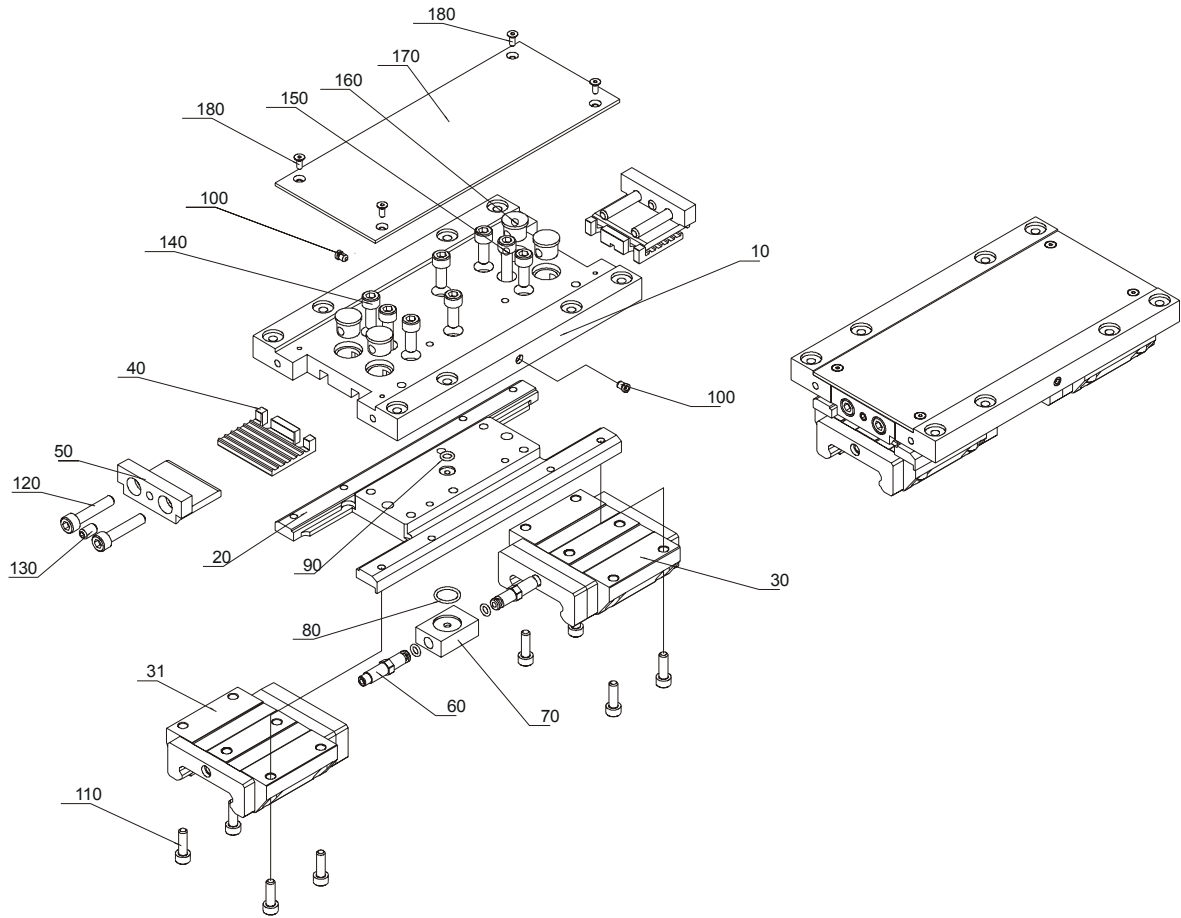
Modul 115/42 Art.-Nr.: 1052929, Exploded view
